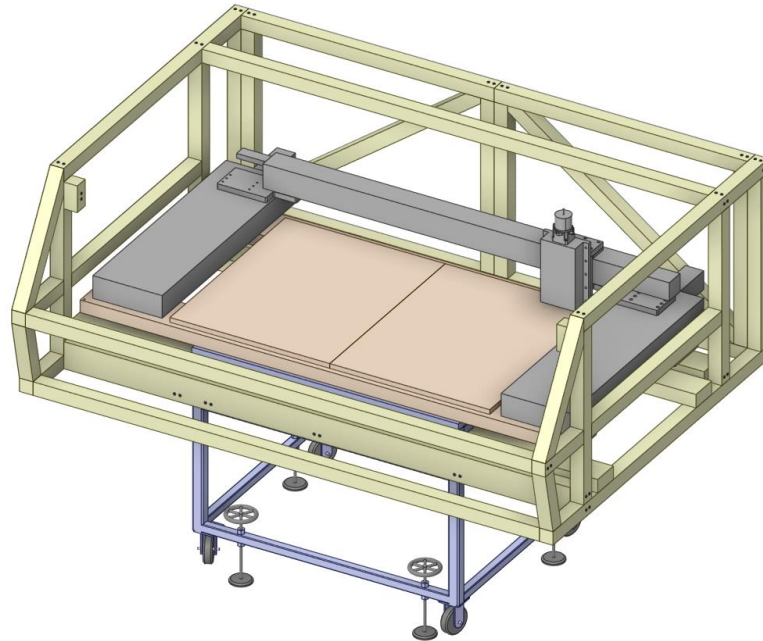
Montaje de los paneles laterales y posteriores a la base de la estructura
